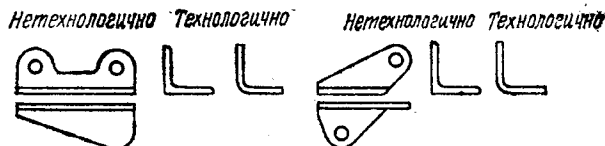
Примеры замены прессованных профилей на профили из листового материала для изготовления соединительных деталей.
